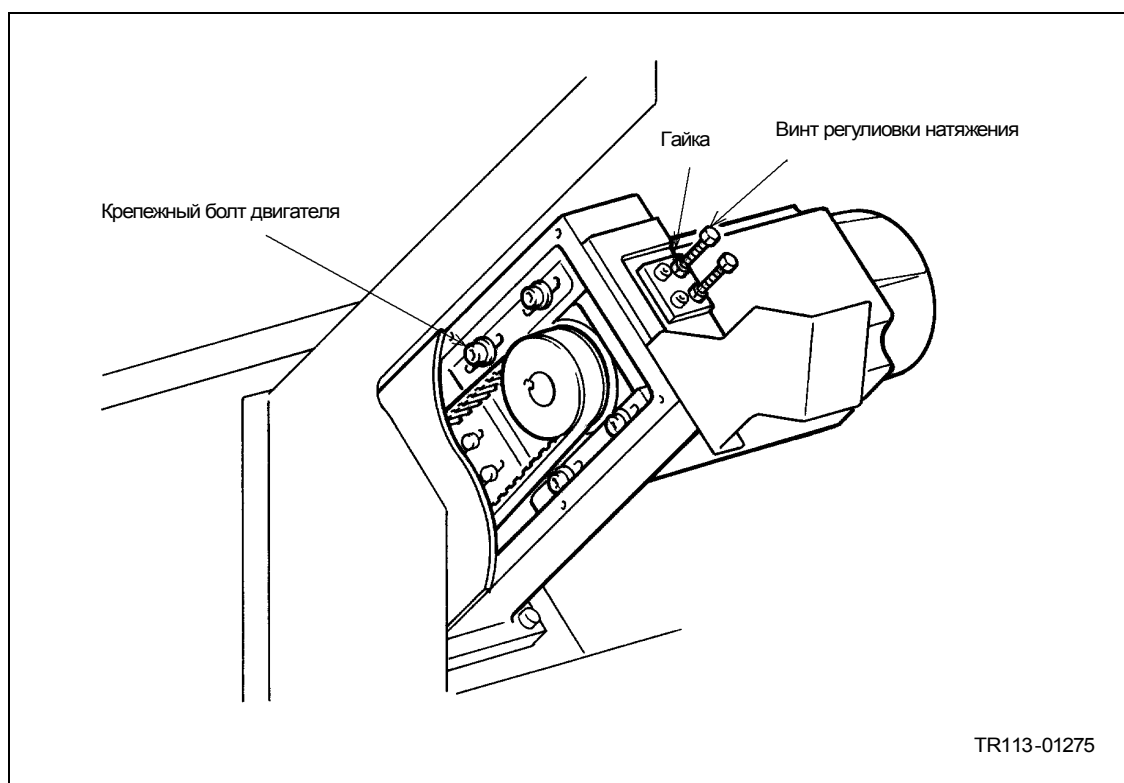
Регулировка ремня фрезерного шпинделя
